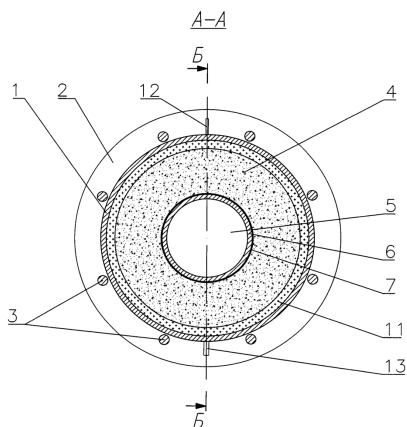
Взрывная камера, вид А-А, сечение Б-Б [6], где: 1 – металлический наружный корпус в форме цилиндра; 2 и 3 – верхние и нижние упорные кольца; 4 – силовой элемент; 5 – рабочая полость; 6 – вставка; 7 – компенсационная прокладка; 11 – гидравлическая камера; 12 – вакуумная трубка; 13 – штуцер.
